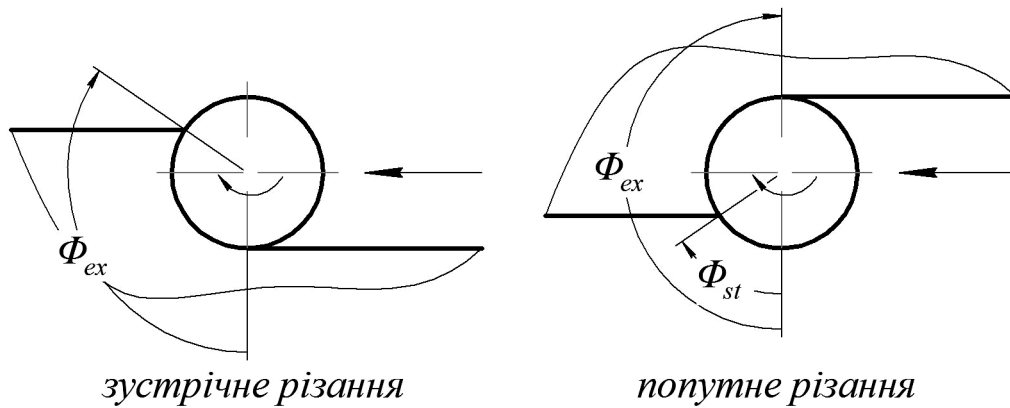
Кути врізання та виходу під час фрезерування циліндричною кінцевою фрезою
